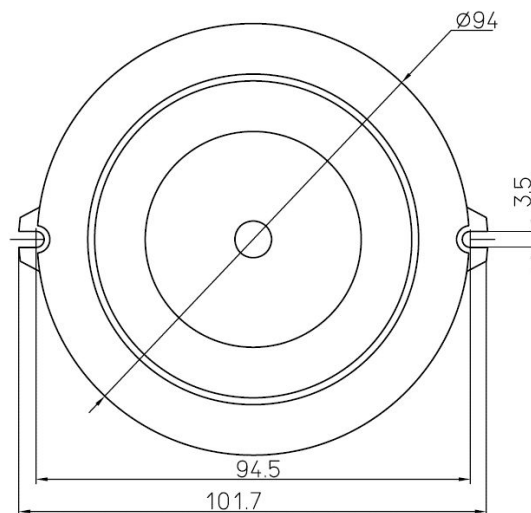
Габаритные и присоединительные размеры корпуса ОСЗ
